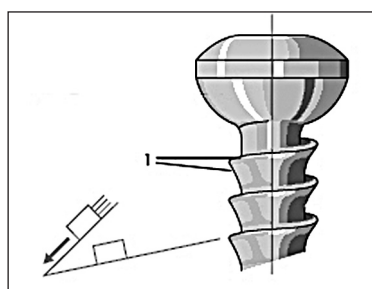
Вид асимметричной резьбы винта: 1 — различный наклон витка резьбы
